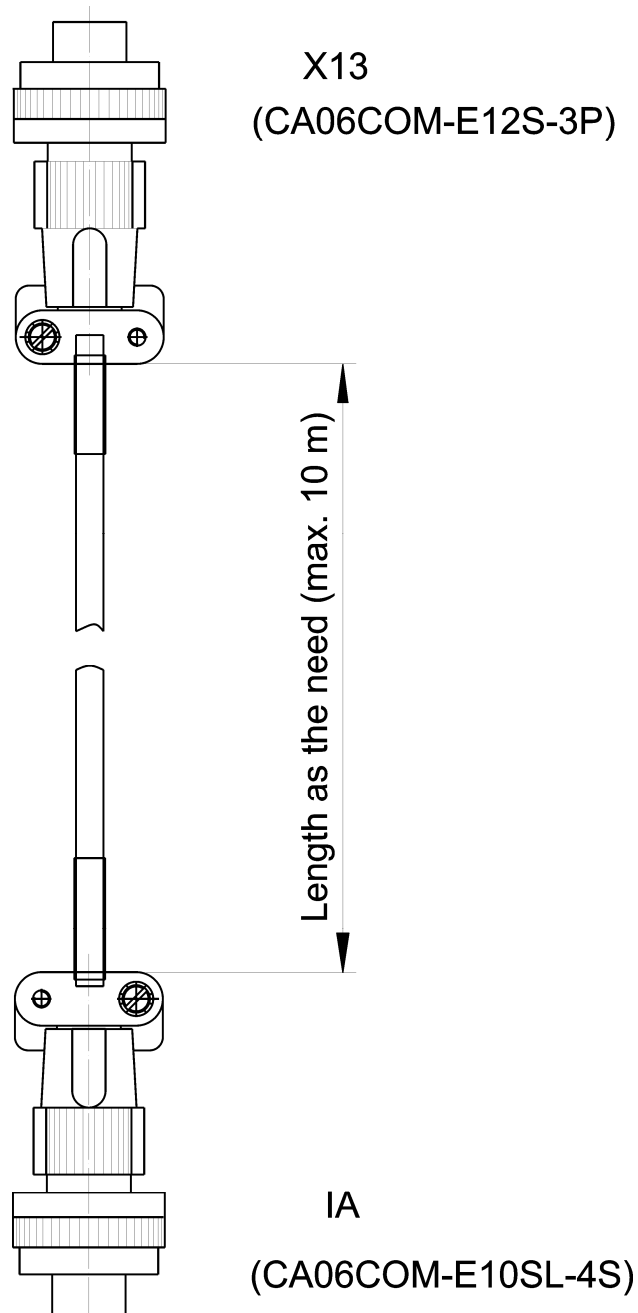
Impulsaufnehmerkabel mit Stecker
